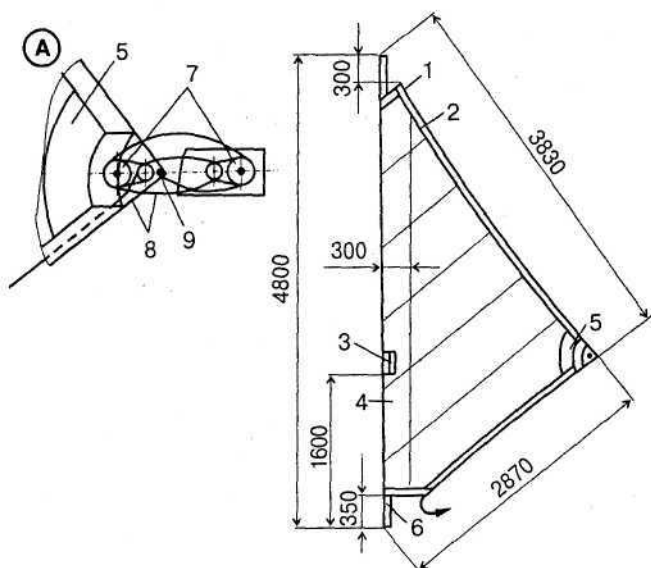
Парус «Стриж»: 1 — нашивки усиления шкаторин паруса; 2 — карман троса задней шкаторины; 3 — вырез под втулку; 4 — мачтовый карман; 5 — боуты шкотового угла; 6 — мачта; 7 — двухслойный блок; 8 — ходовой конец; 9 — заделка конца в шкотовом углу паруса; А — таль регулировки «пуза» паруса
